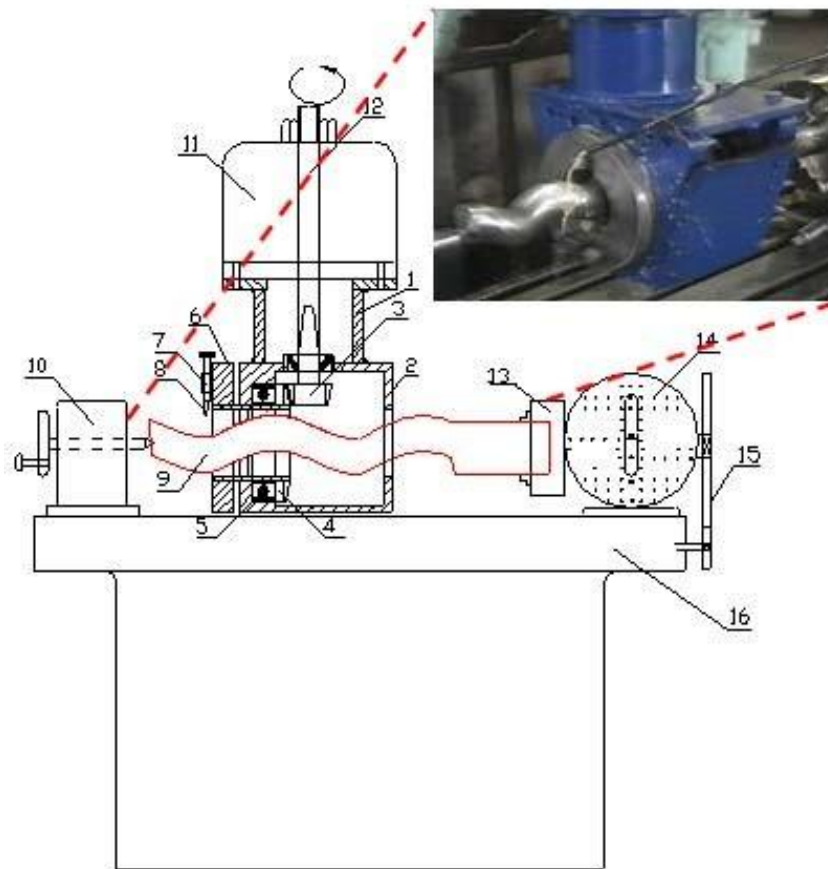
Dispositivo especial FRETOR instalado en una fresadora universal.
